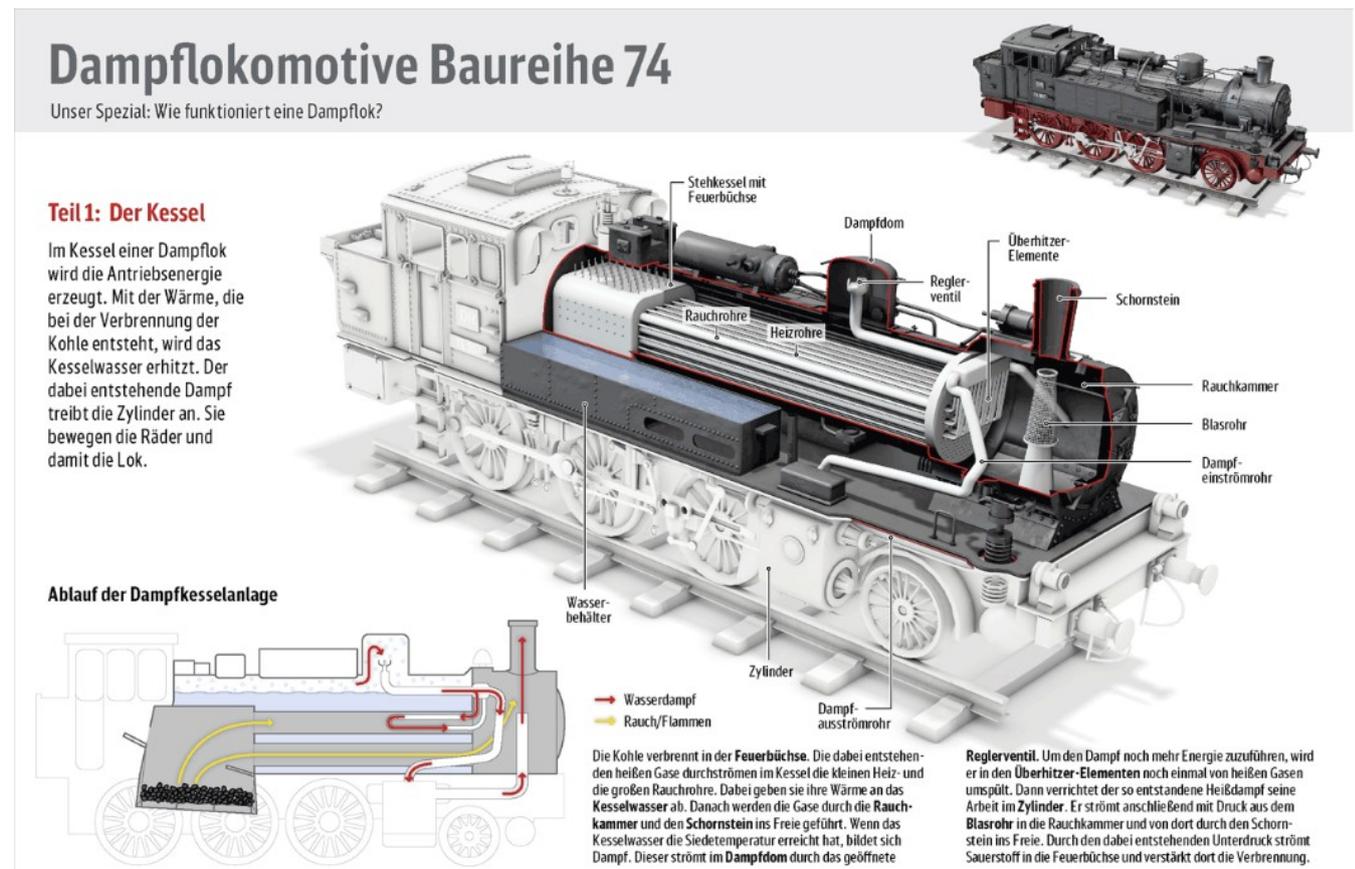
Wie funktioniert eine Dampflok Baureihe 74?
